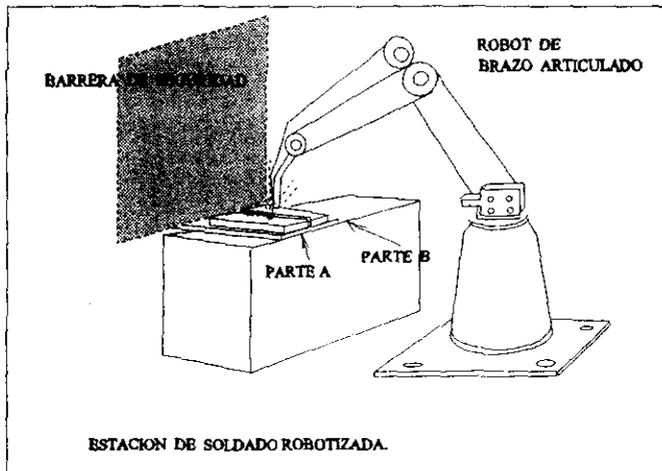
SOLDADURA POR ARCO MEDIANTE ROBOT INDUSTRIAL
